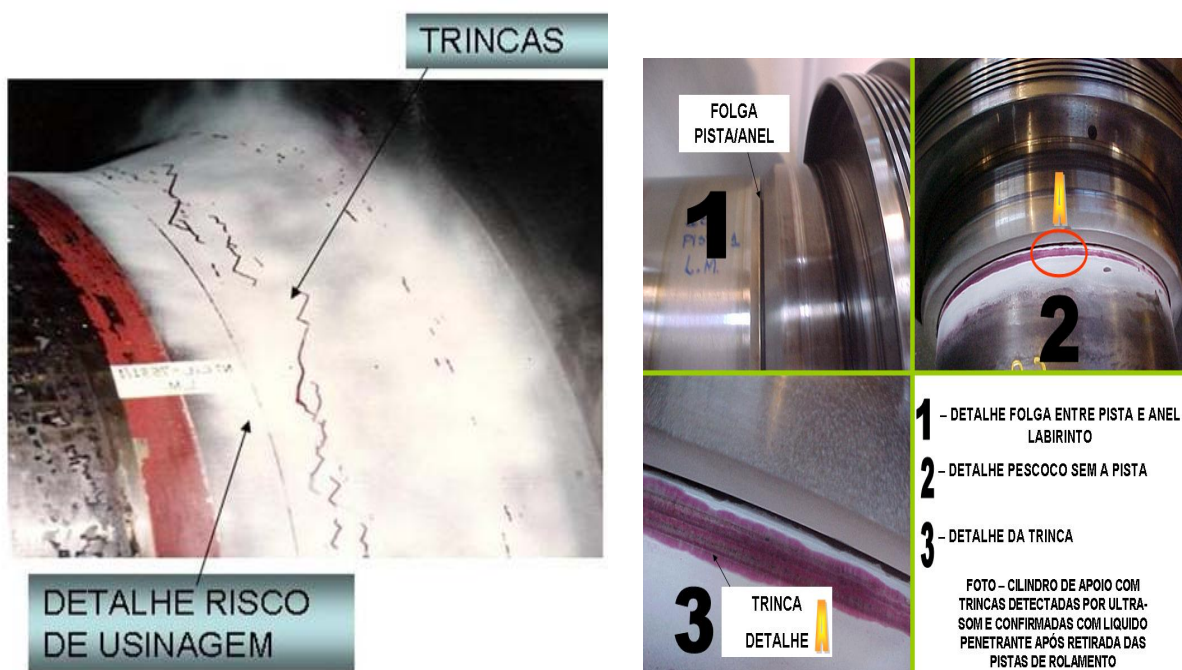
Trincas detectadas por ultra-som abaixo do anel labirinto e pistas de rolamento
